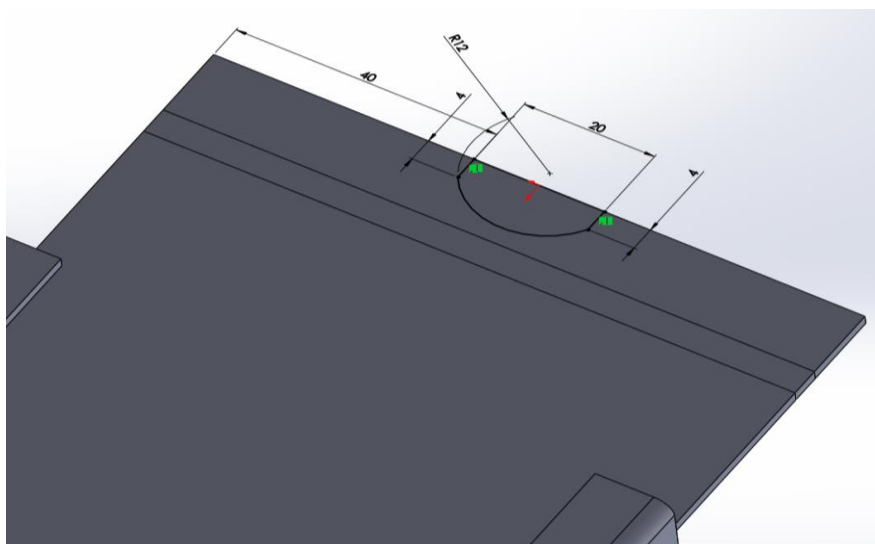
Schița necesară pentru operația de extrudare-taiere (extruded-cut)
